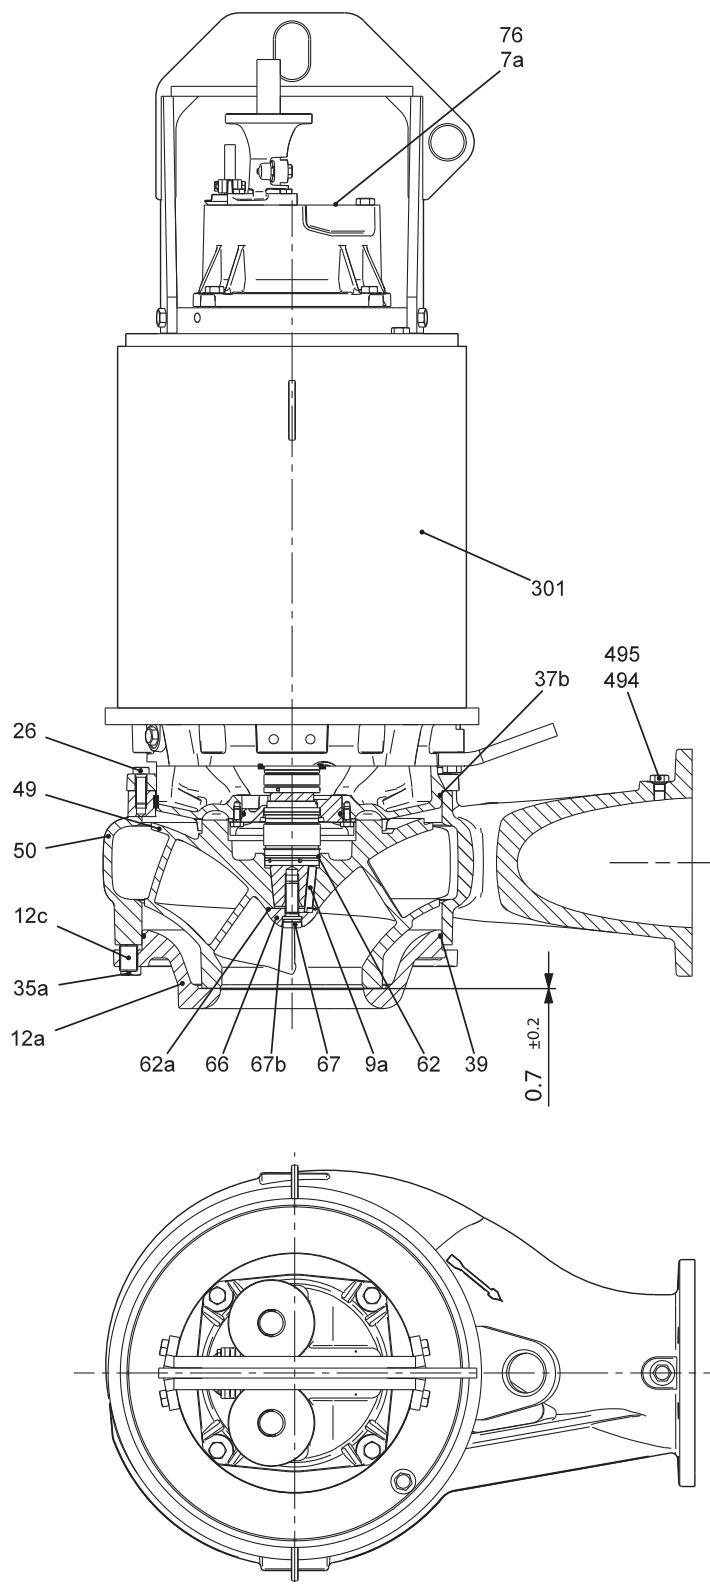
Взрывозащищённый двигатель без охлаждающего кожуха
